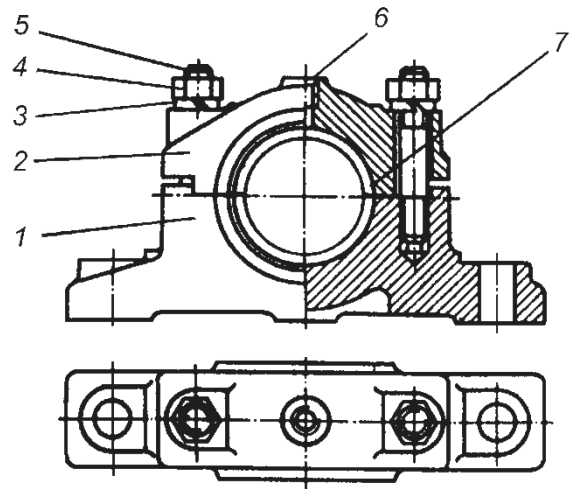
Конструкция разъемного подшипника скольжения с плоскостью разъема, параллельной плоскости основания корпуса:
